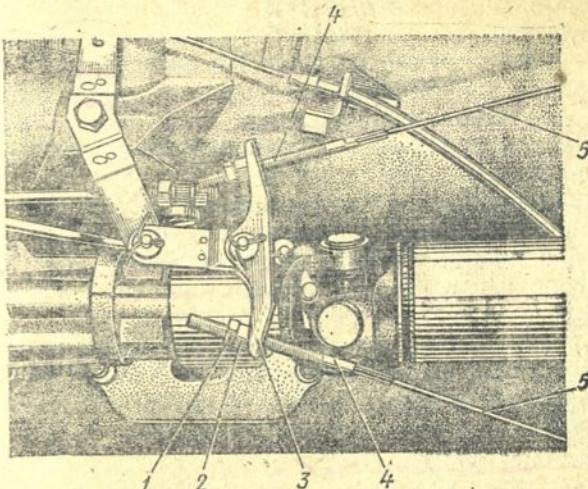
Регулировочный узел привода стояночной тормозной системы:
